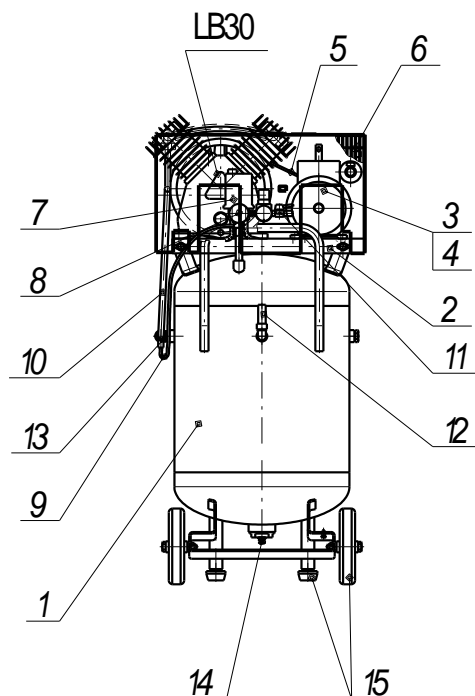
Общий вид компрессора СБ4/С-100.LB30В, СБ4/С-100.LB30АВ
